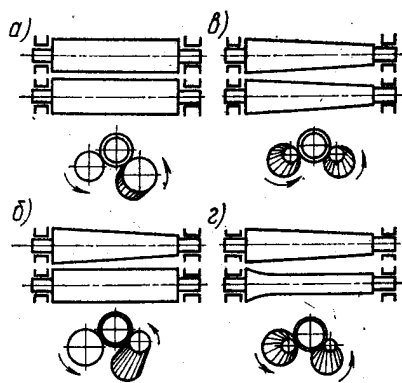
Схемы расположения двух валков в загрузочных приспособлениях
